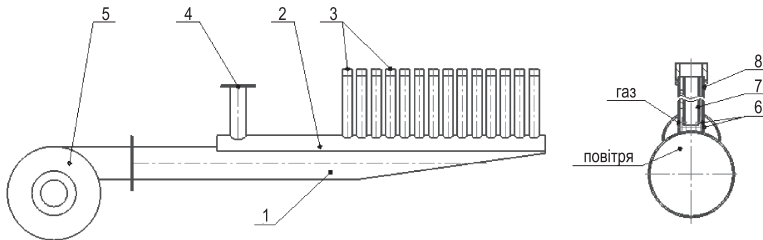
Пальник газовий багатосопловий попереднього змішування: 1 – повітряна камера; 2 – газорозподільна камера; 3 – змішувач газу і повітря; 4 – штуцер для підведення газу; 5 – вентилятор; 6 – отвори; 7 – вставка; 8 – насадка.
